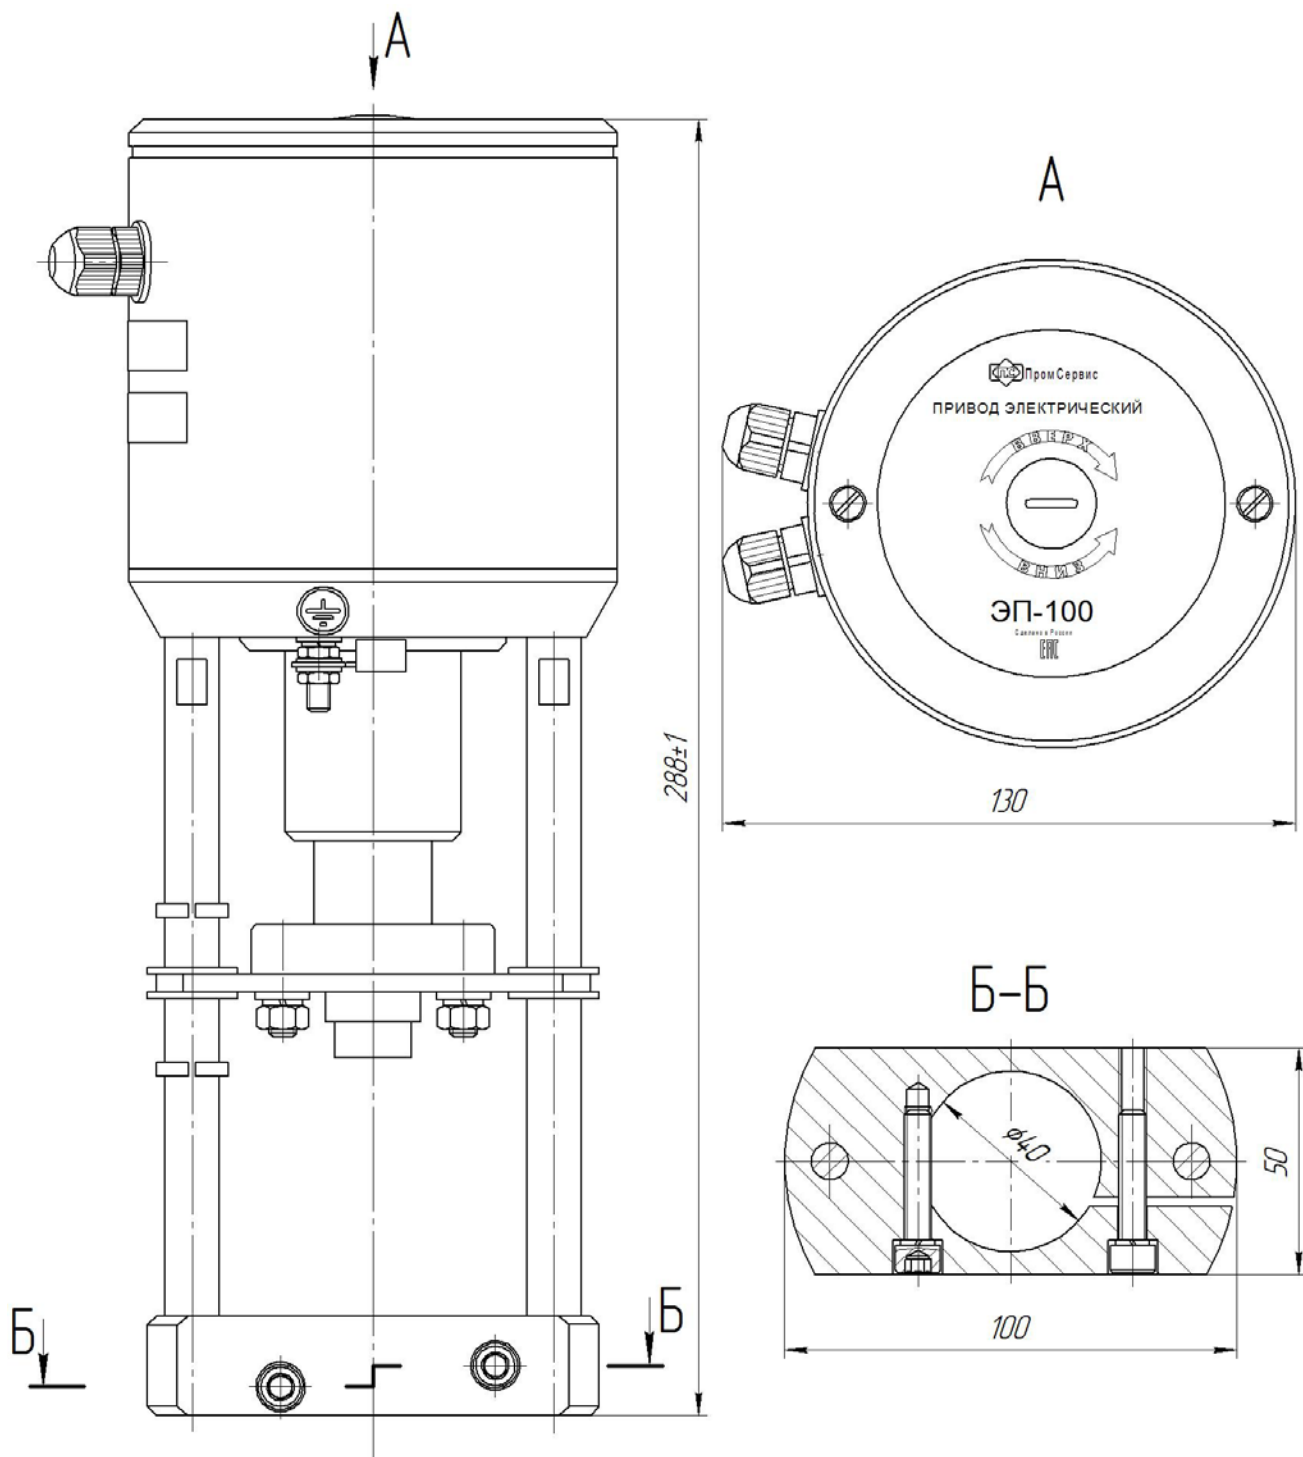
Габаритные и присоединительные размеры привода исполнения ЭП-100-01
